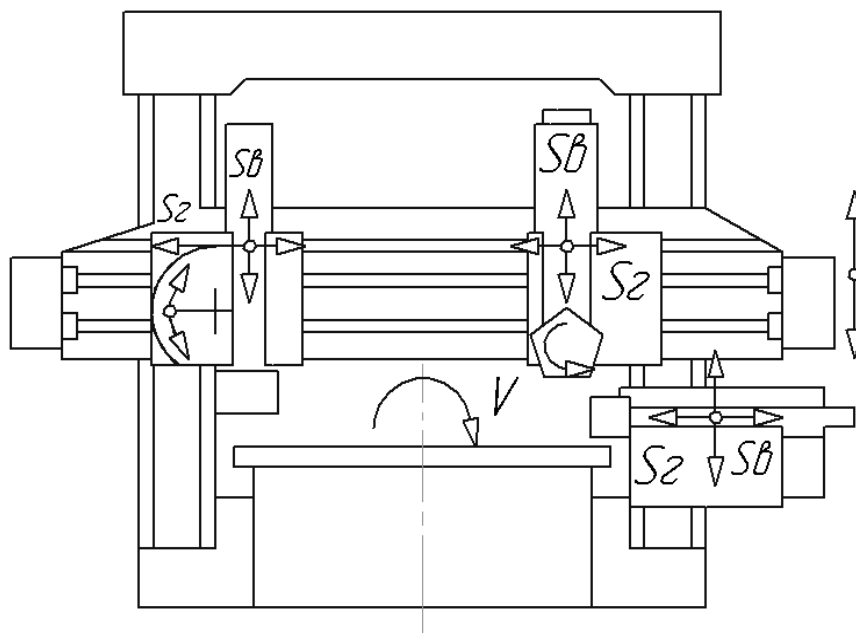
Загальний вигляд токарно-карусельного верстата
